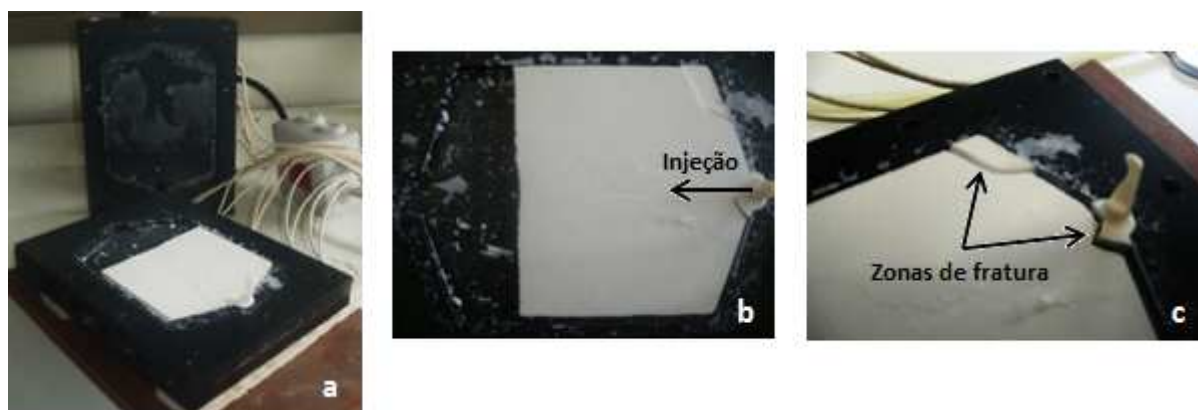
Primeira placa produzida de pCBT puro: a - molde aberto com placa de pCBT puro no seu interior; b – sentido de injeção da resina; c - pormenor das zonas de fratura.
